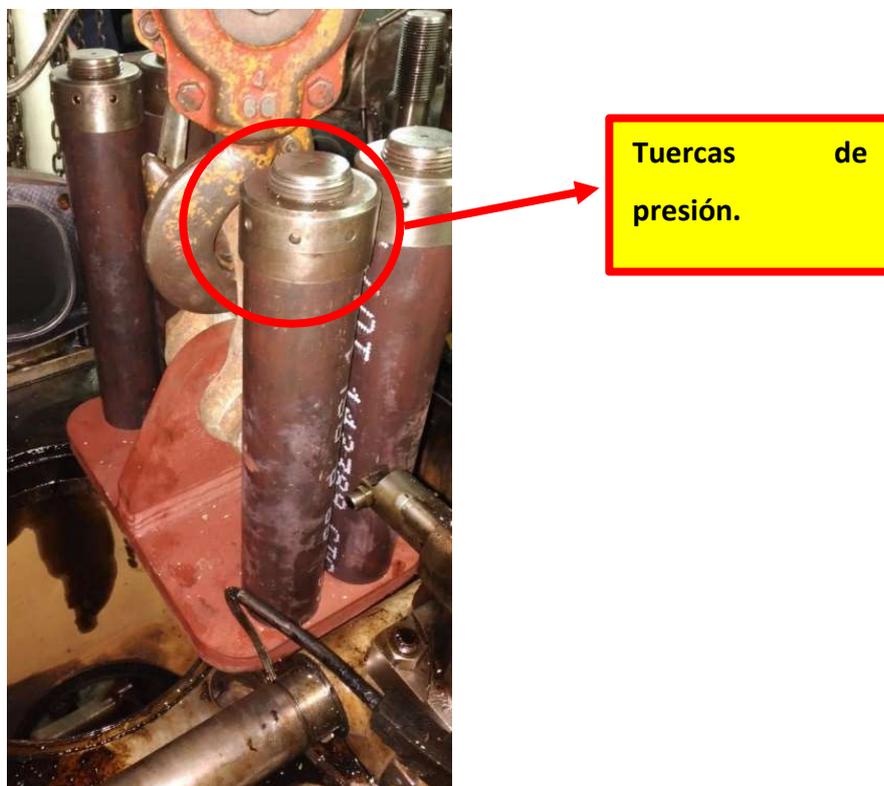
Detalles de útiles empleados para el izado. Fuente: Trabajo de campo.
